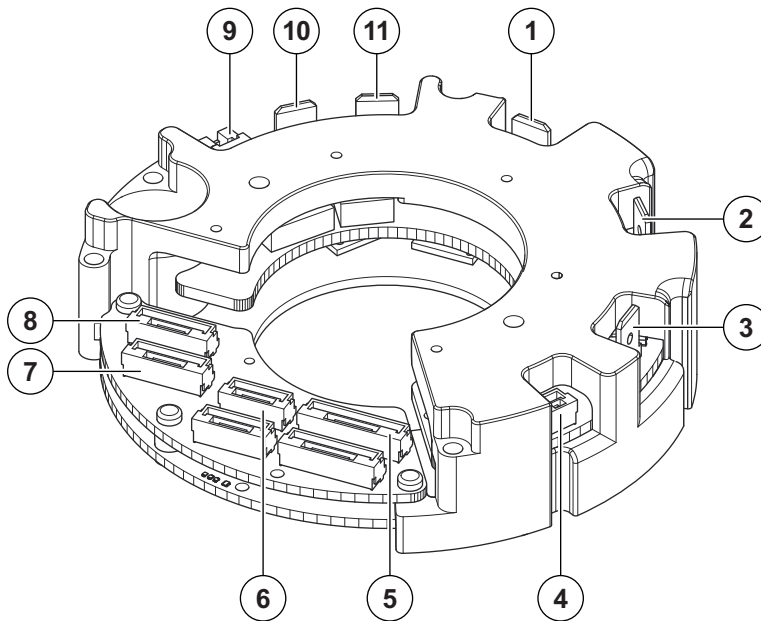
Anschlüsse TUAKA DRIVE (Beispielabbildung)
